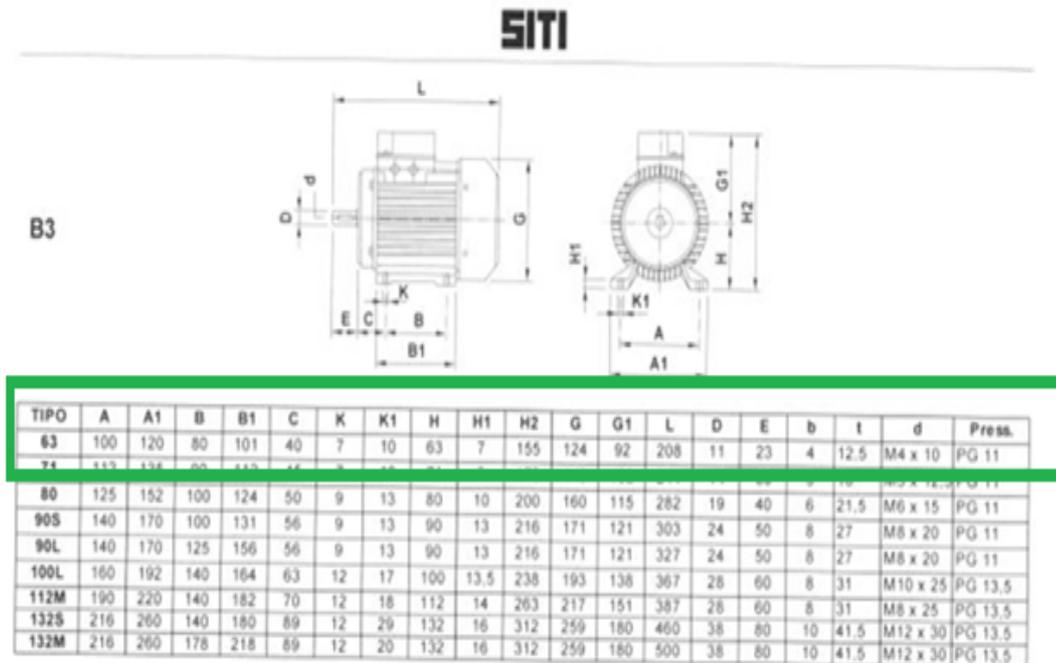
Dimensiones del motor que origina vaivén en el conjunto cuchilla de producto.
